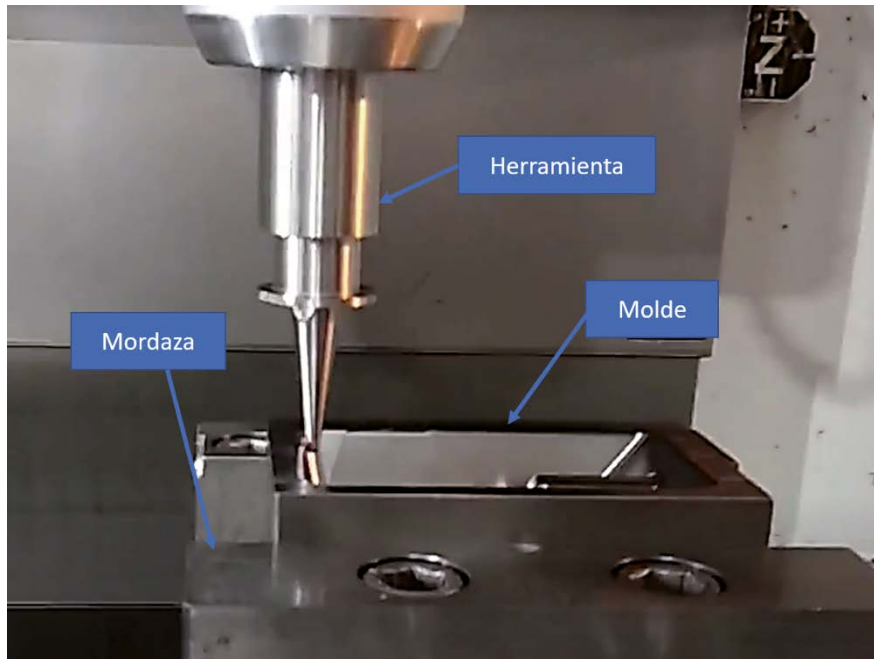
Herramienta fabricada instalada en una fresadora sobre el molde objeto de ensayo.
